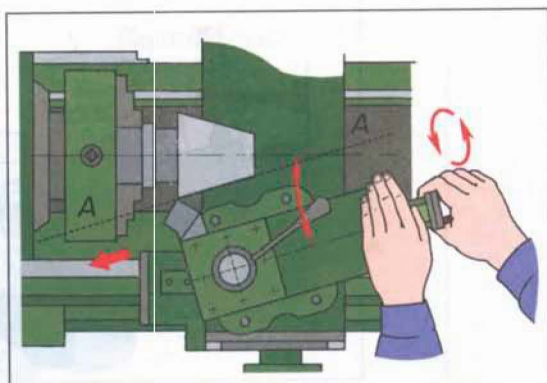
Получение конусной поверхности на детали путём поворота верхней части суппорта токарного станка
